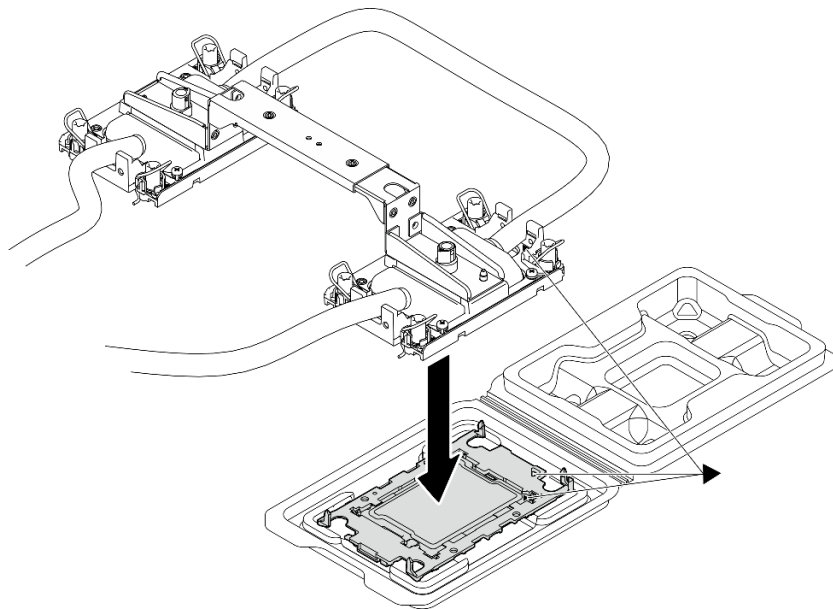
Montieren des Prozessors mit Kühlplatte
